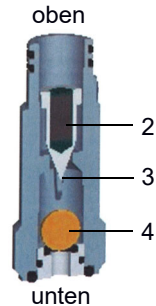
Querschnitt Kugelrückschlag-Gehäuse
